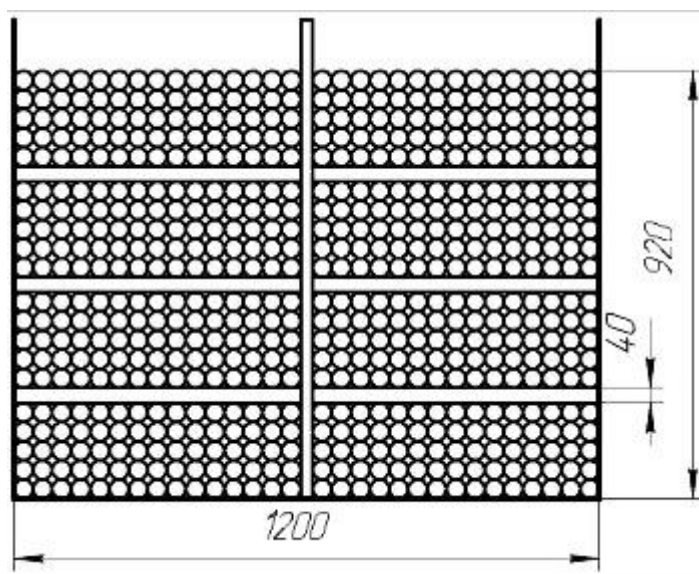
Схема сборки сортового проката из быстрорежущей стали
